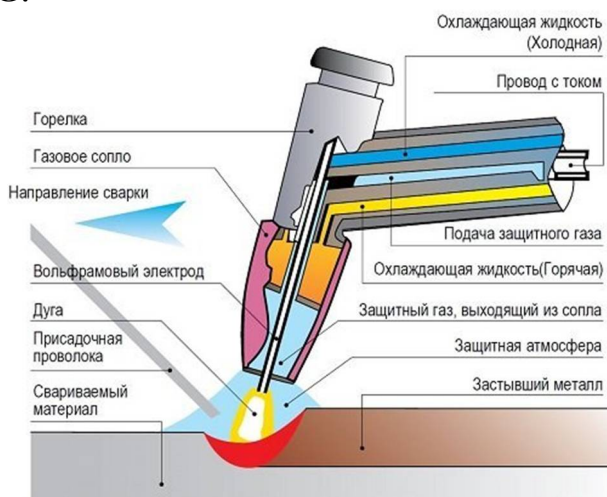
Принцип работы аргонодуговой сварки
